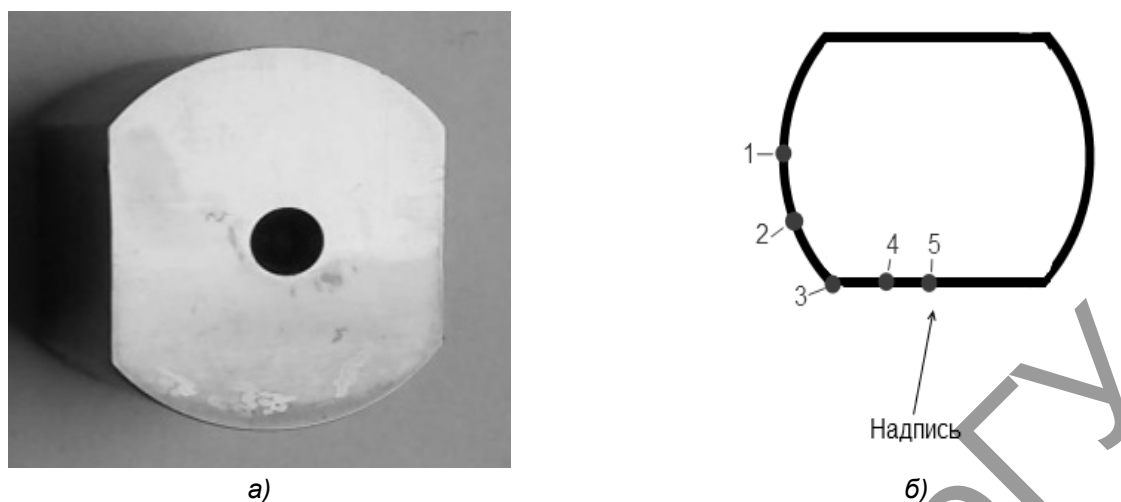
Экспериментальный образец сплава ТС4: а — внешний вид шлифа; б — схема измерения микротвердости *HV* шлифованных образцов из титанового сплава ТС4
